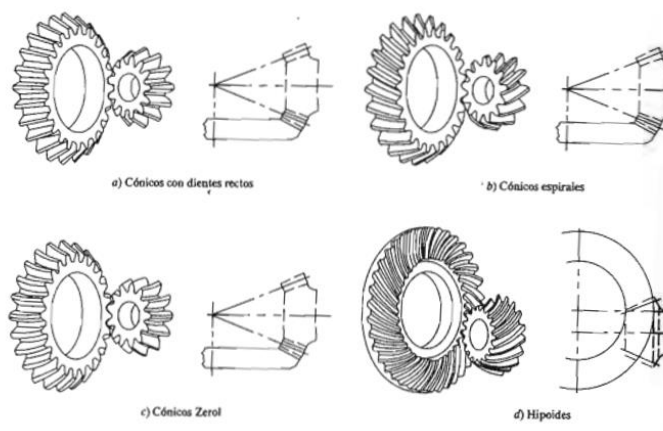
Tipos de Engranajes Cónicos. Fuente: R. L. Mott, 2006.
